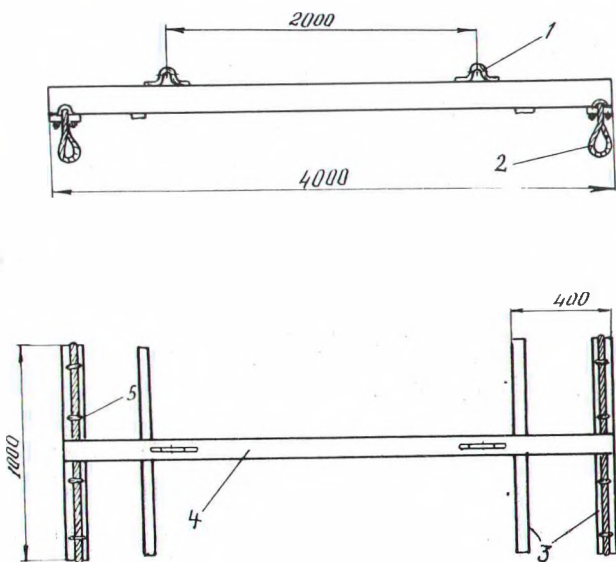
Погрузочно-разгрузочное устройство: 1 – скоба; 2 – петля; 3 – поперечные балки; 4 – продольная балка; 5 – зажим
